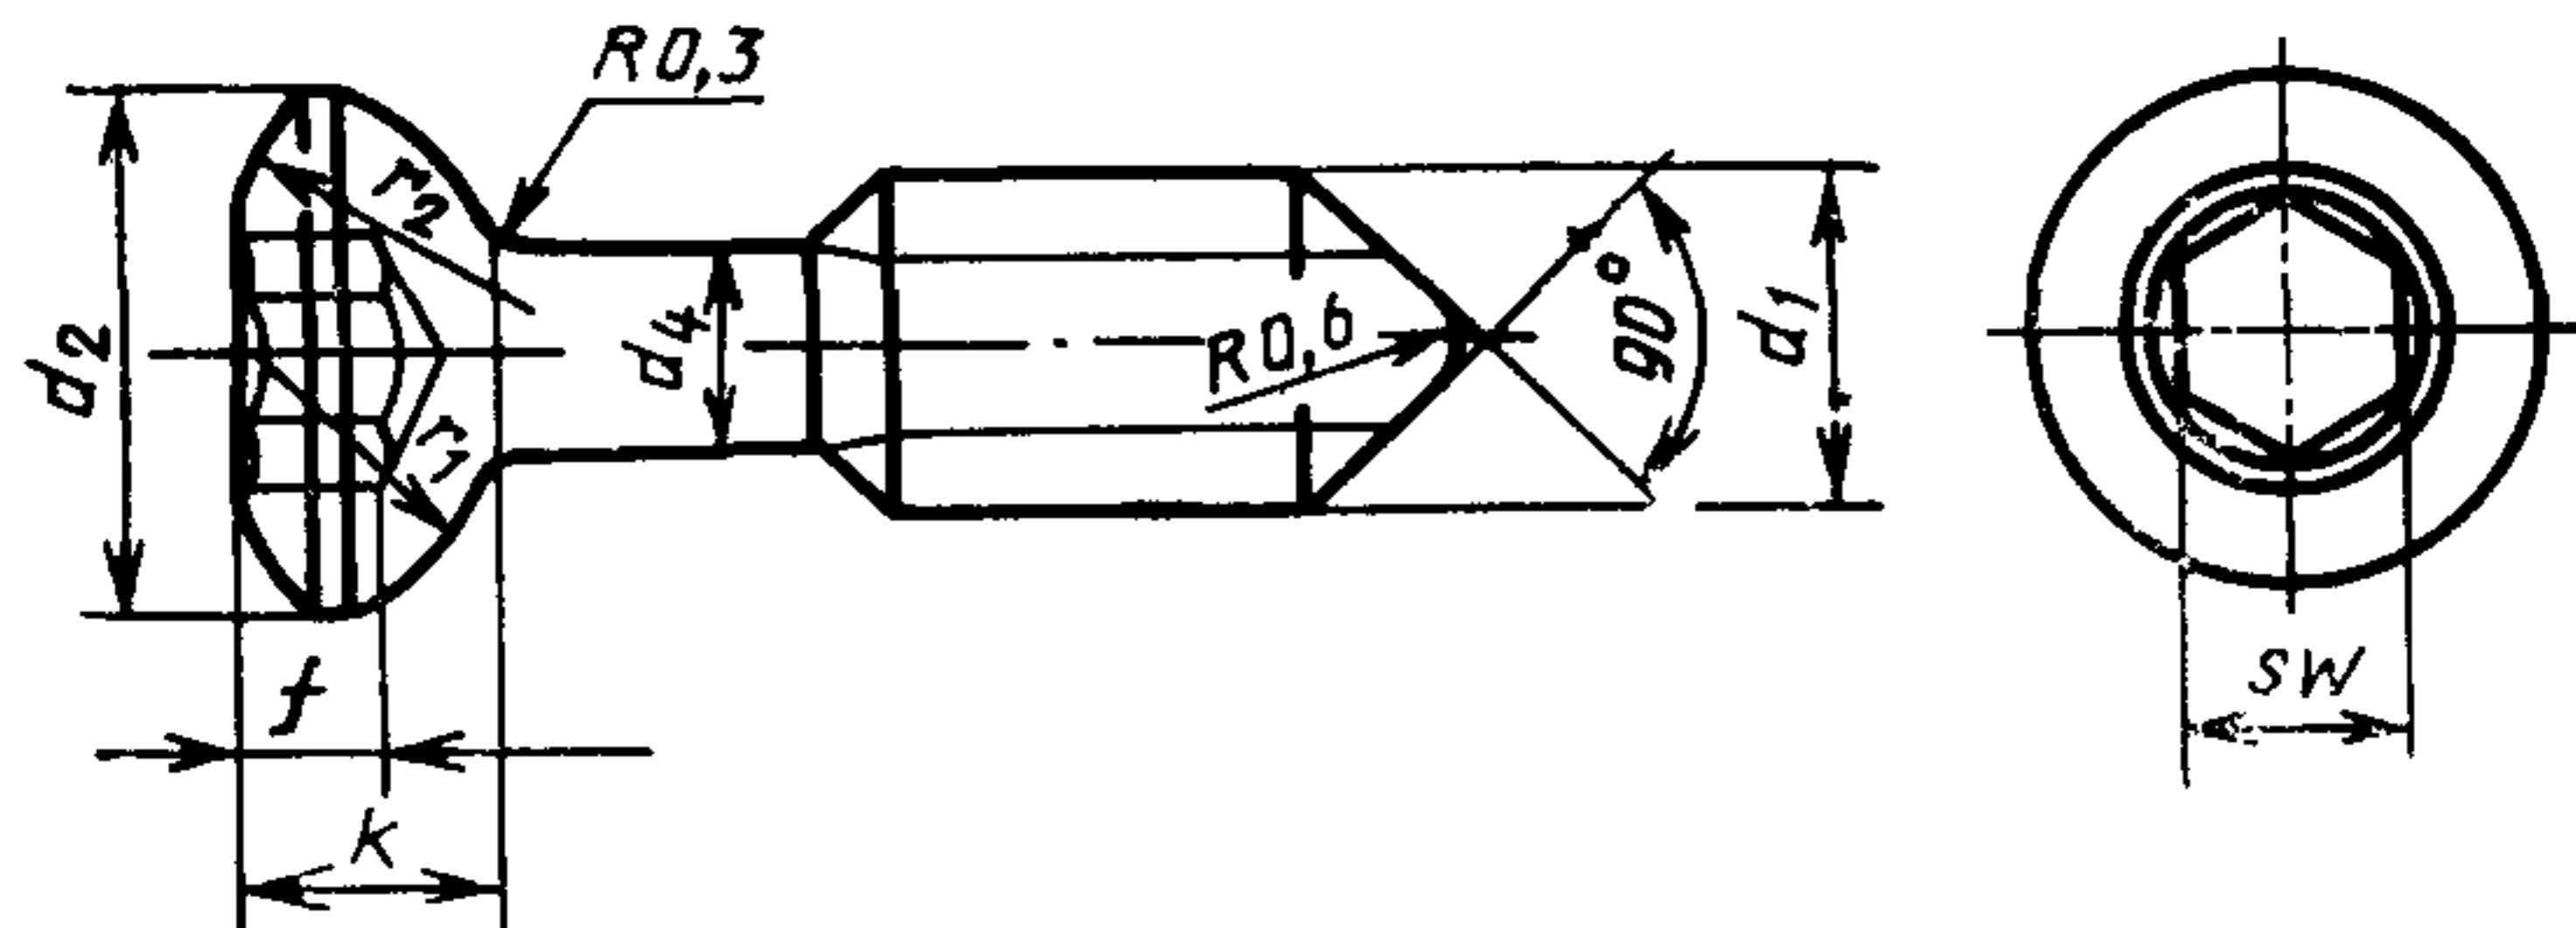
Шуруп с глубокой резьбой (НВ)
